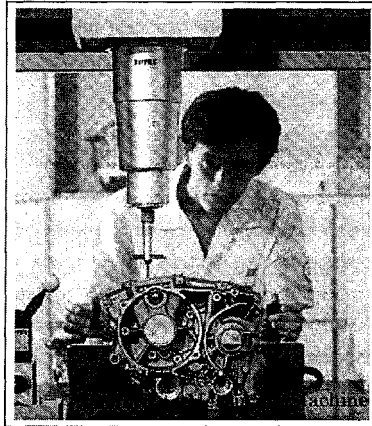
Chinesisches Unternehmen der Kfz-Industrie mit moderner Meßmaschine
